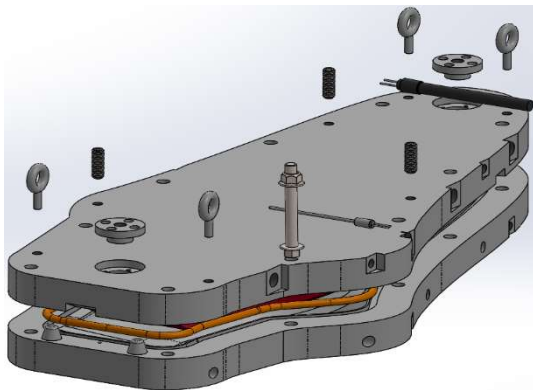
Molde calefactado para manufactura del álabes por RTM.
